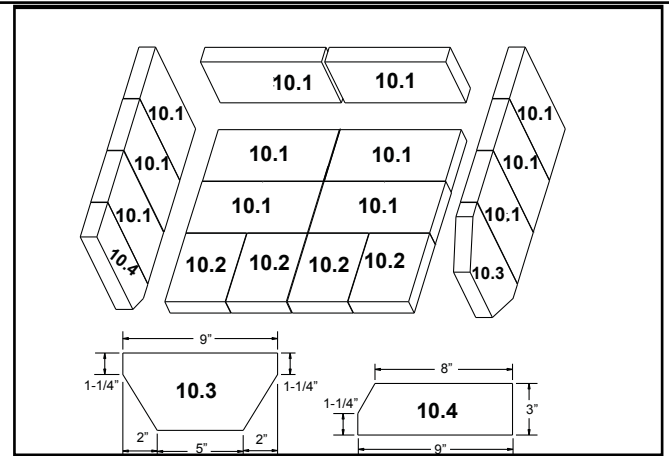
Ensemble de briques pour le Millennium 3100
